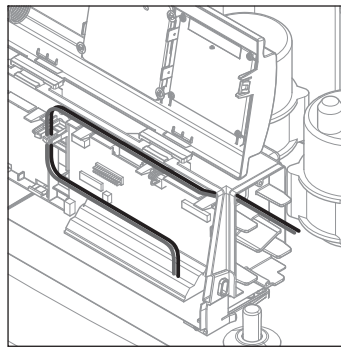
5. Posare i cavi nella regolazione e realizzare i collegamenti elettrici (vedere sezione 2.4.2).
